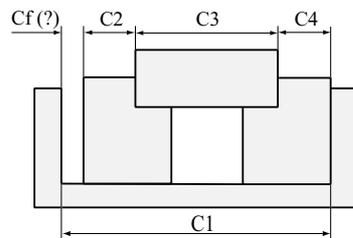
Representación de un caso de análisis de dimensiones y tolerancias
